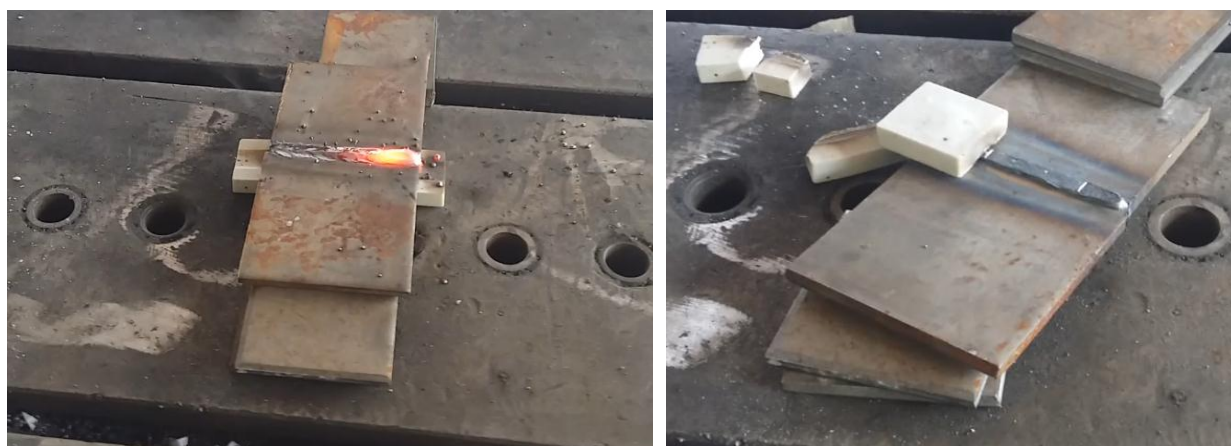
Внешний вид подкладок до и после формирование сварочного шва.
